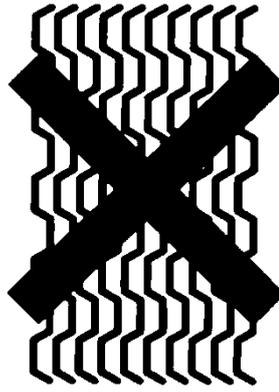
Вид на пакет пластин при неправильной сборке
